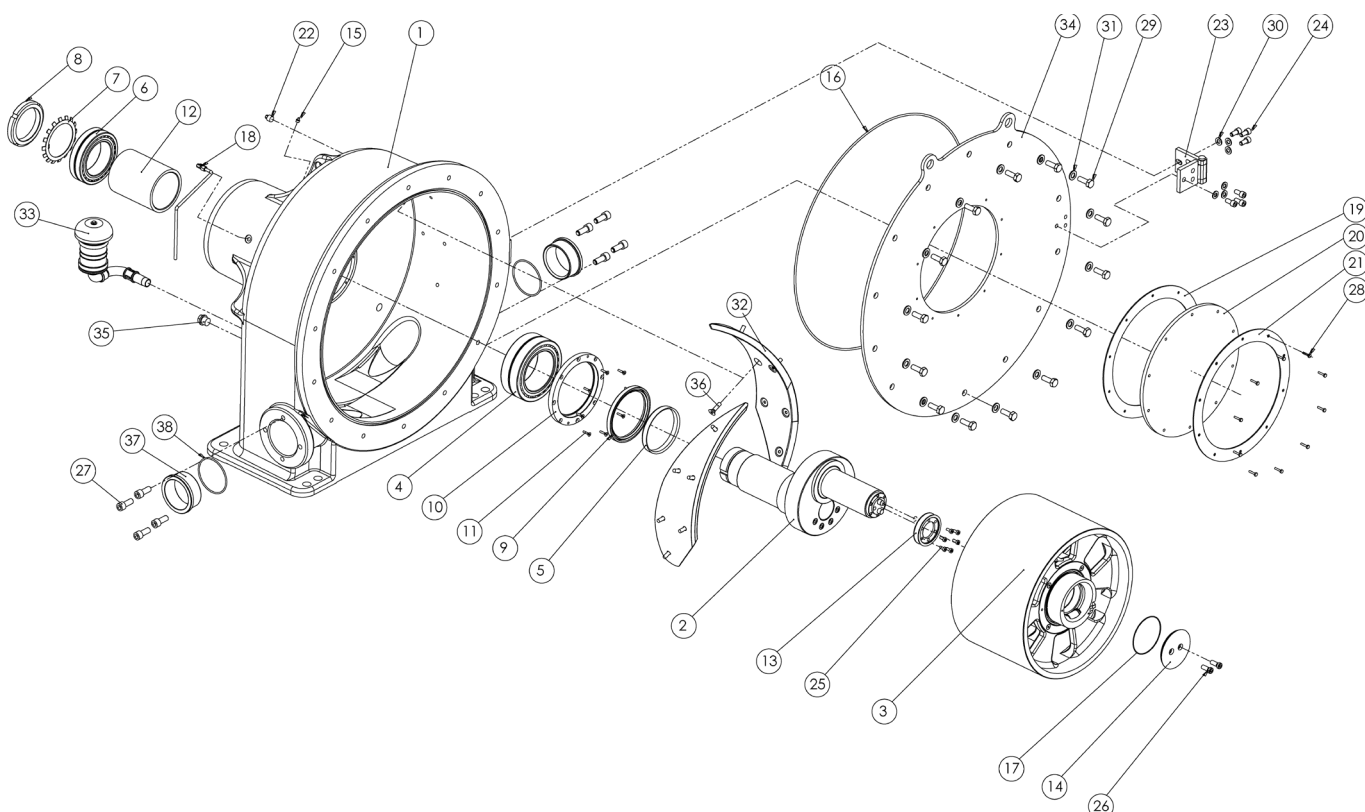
Explosionszeichnung des LPP-T-Pumpenkopfs
